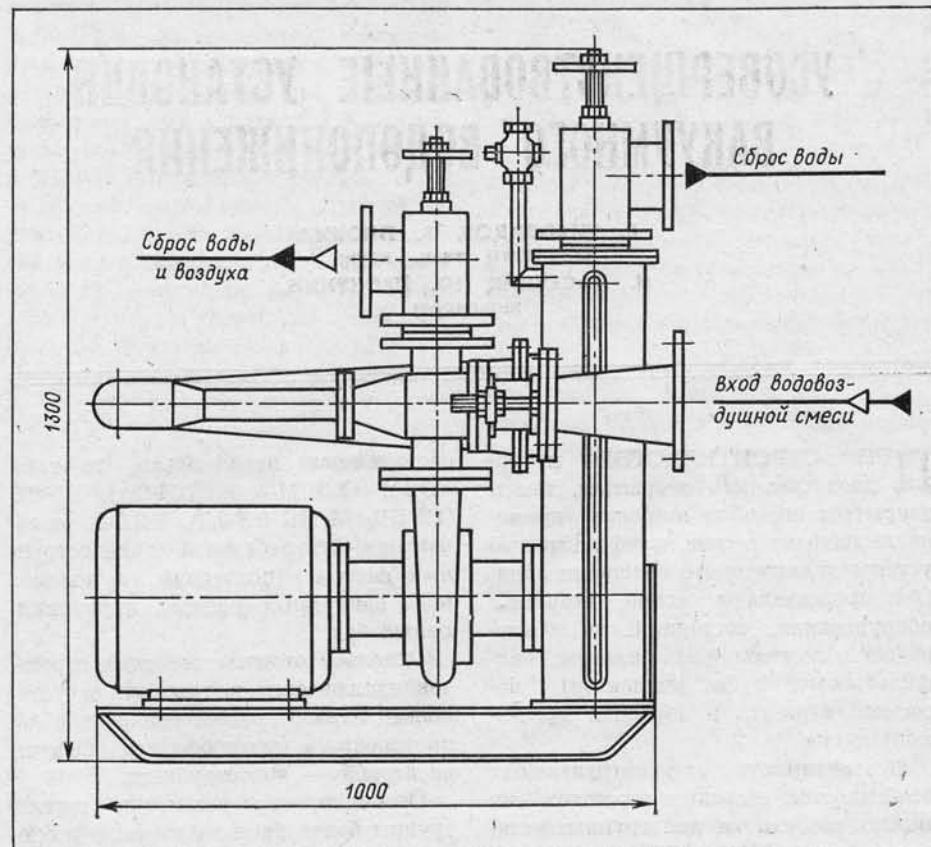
Силовой агрегат установки УВБУ-90-35.
